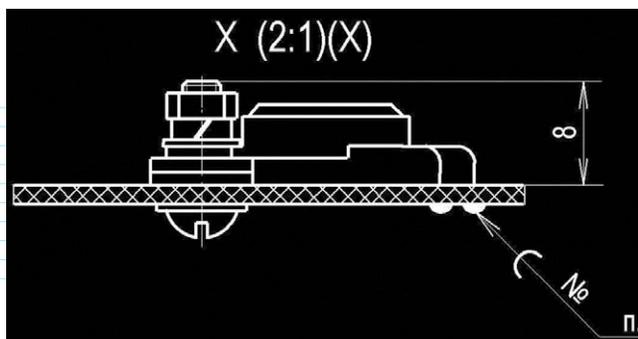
Чертеж установки компонента (Mounting) на печатной плате
